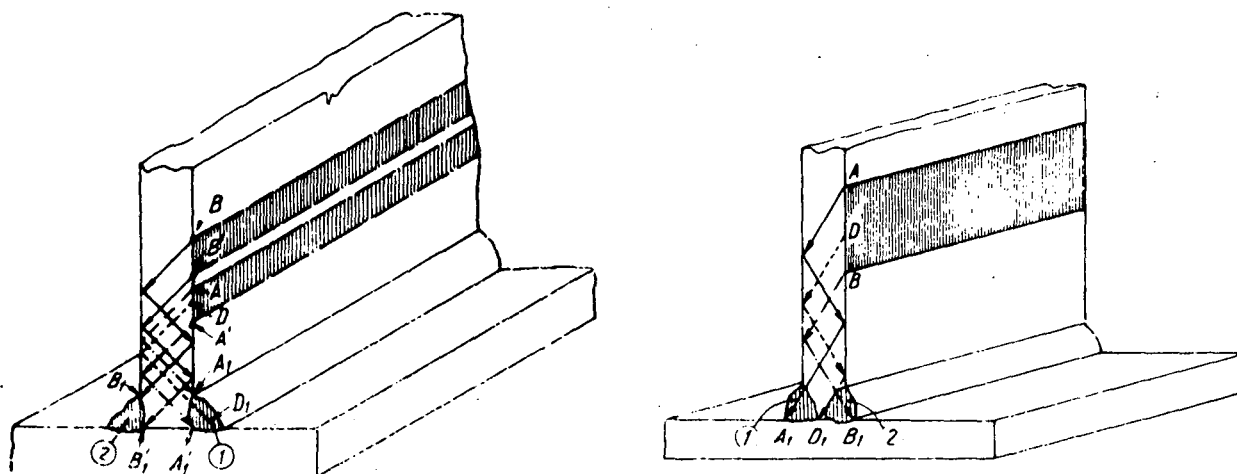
Examen de soldaduras en ángulo. Esquema de exploración o barrido.
